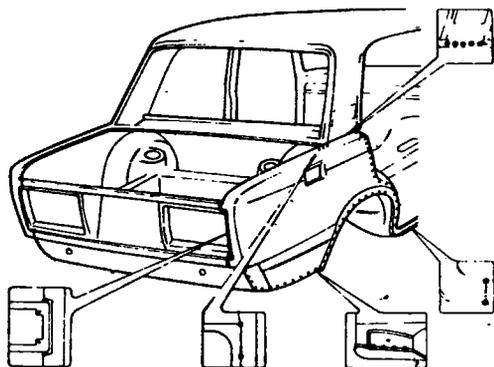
Места сварки заднего крыла. На основном виде точками обозначены швы контактной сварки. На фрагментах показаны места газовой сварки
